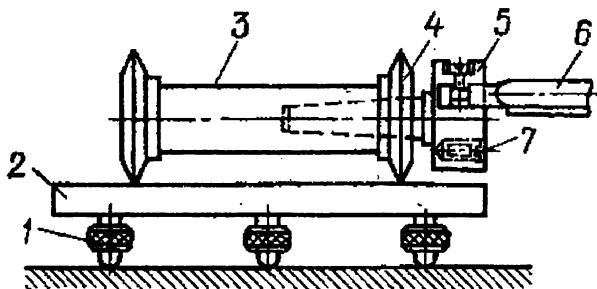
Приспособление для статической балансировки концевых фрез с патроном:
